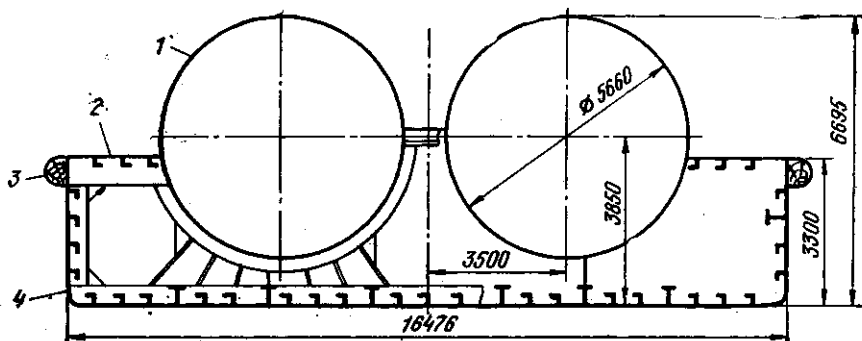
Мидель-шпангоут наливной баржи с двумя цилиндрическими оболочками (пр. 16 802):
